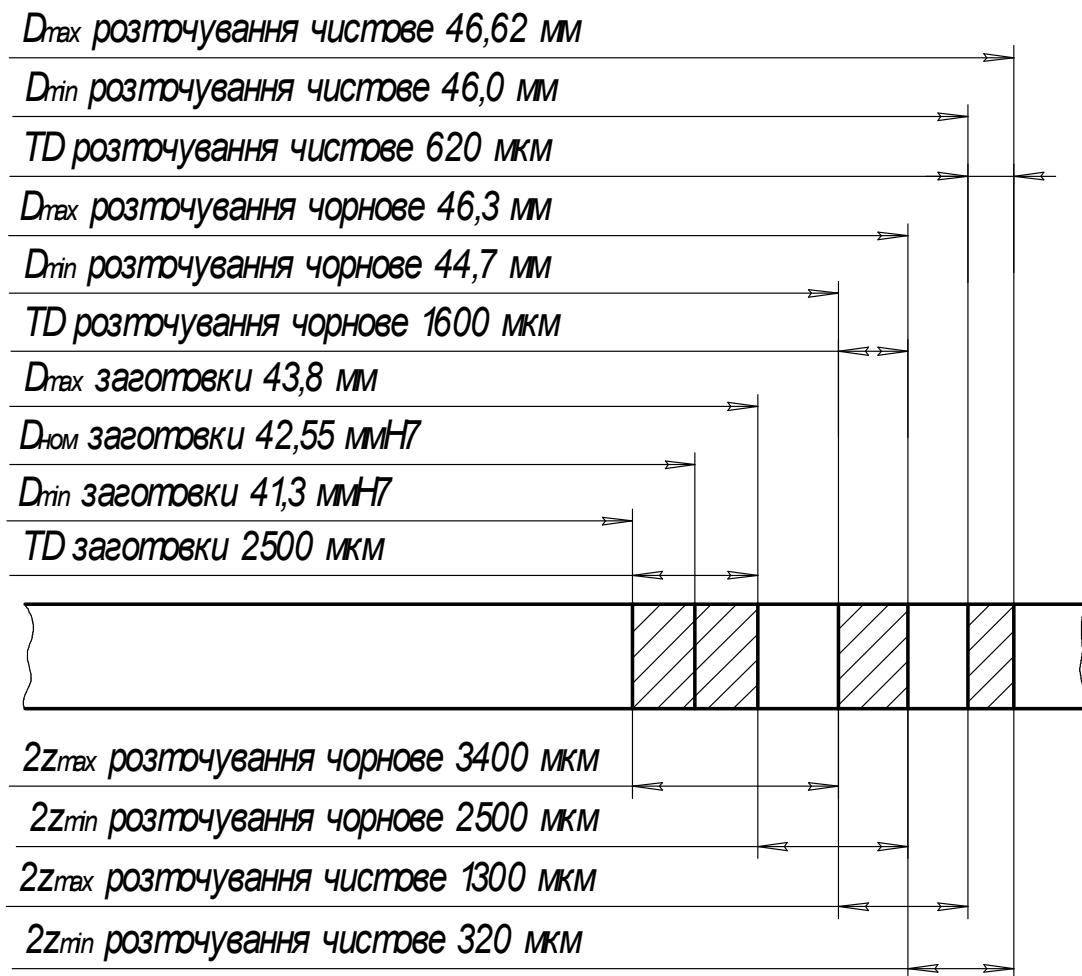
Схема розташування припусків та допусків
